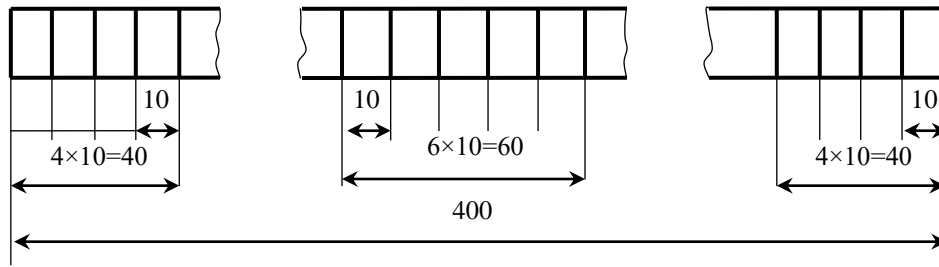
Схема расположения отверстий в неподвижной пластине из стали 65Г (модифицированный метод вставок)
